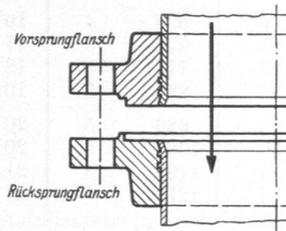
Flansch mit Eindrehung für Flachdichtung DIN 2513.
